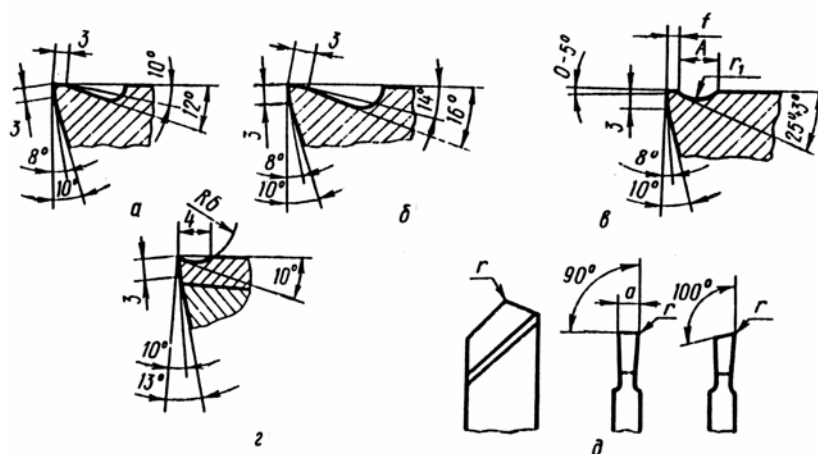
Формы передней поверхности резцов из быстрорежущей стали
